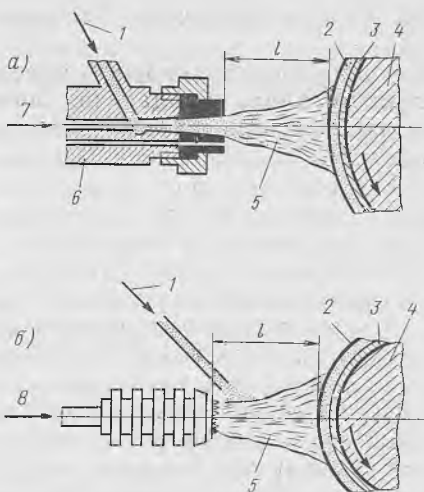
Принципиальная схема подачи порошка при газопламенном напылении: а — инъекцией струи кислорода; б — силами гравитации; 1 — подача порошка; 2 — напыленный слой; 3 — подслой; 4 — деталь; 5 — факел пламени; 6 — горючая смесь; 7 — транспортирующий газ; 8 — подача рабочего газа; l — дистанция напыления
